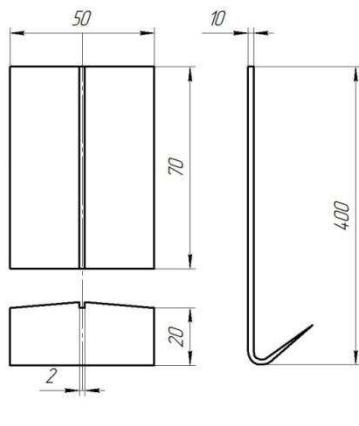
Вспомогательный инструмент: а – дорожник, б - разгонка
